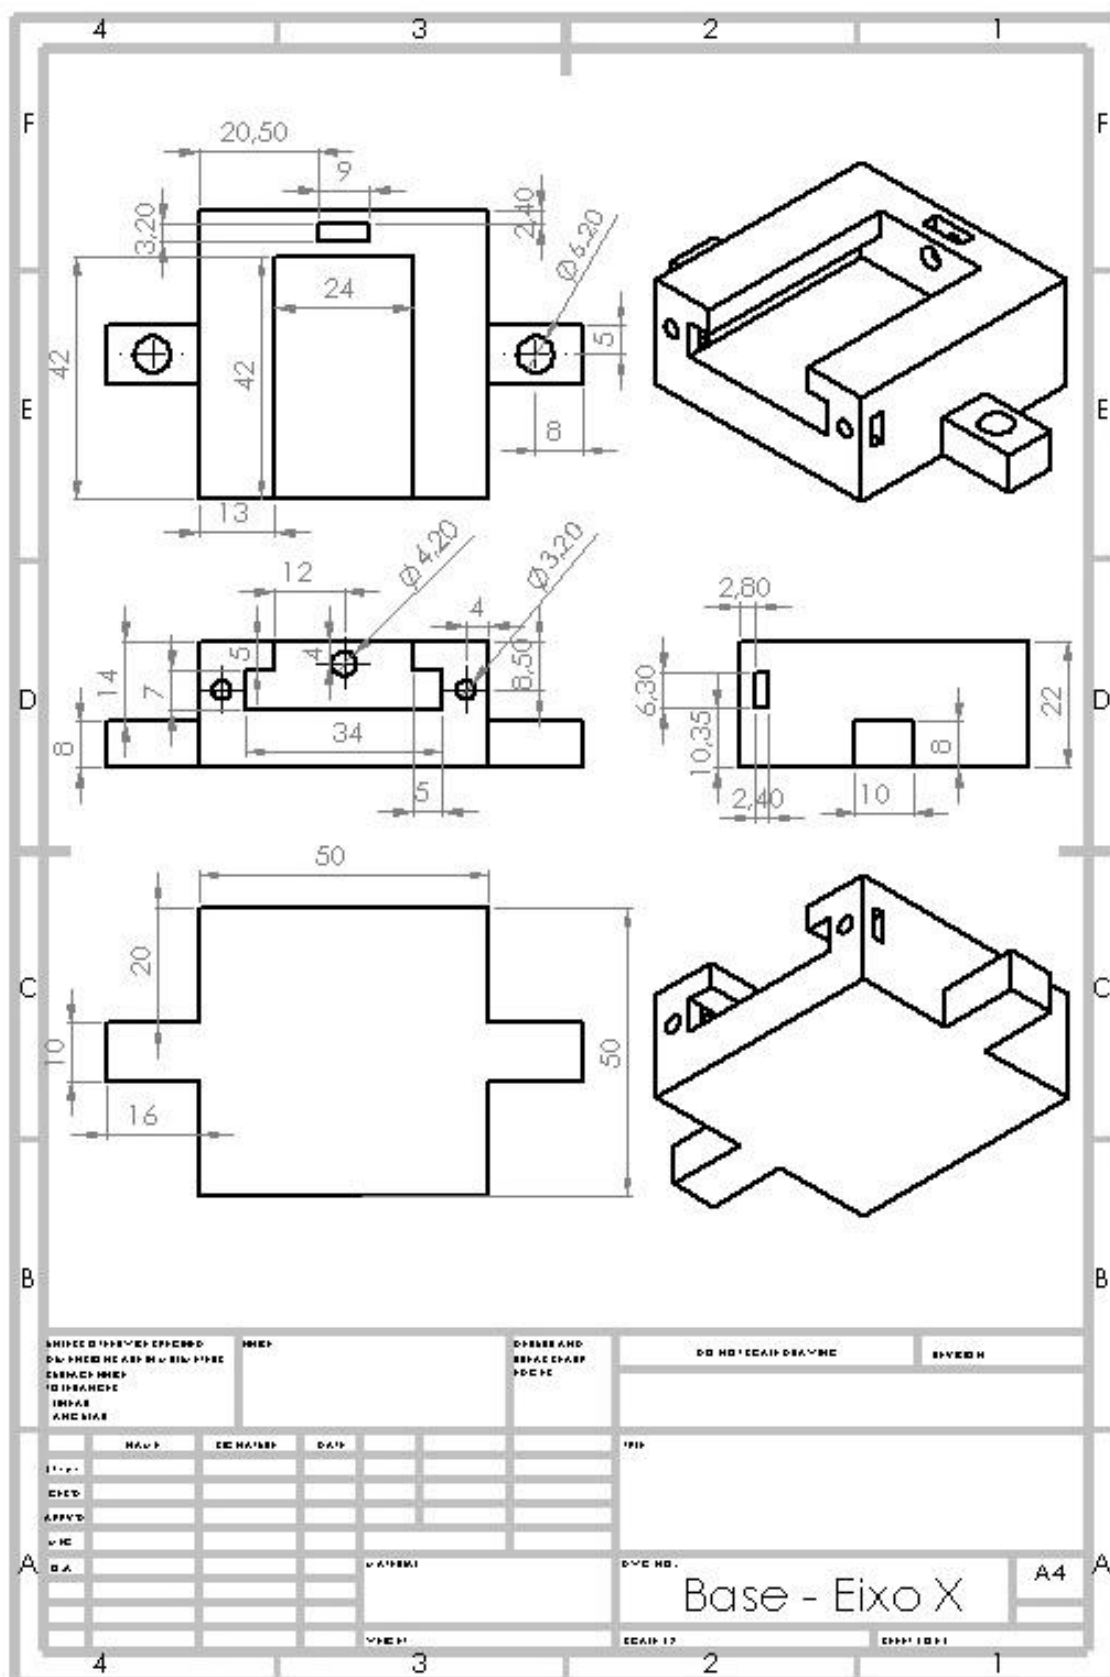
Desenho técnico da peça Base-Eixo X.
